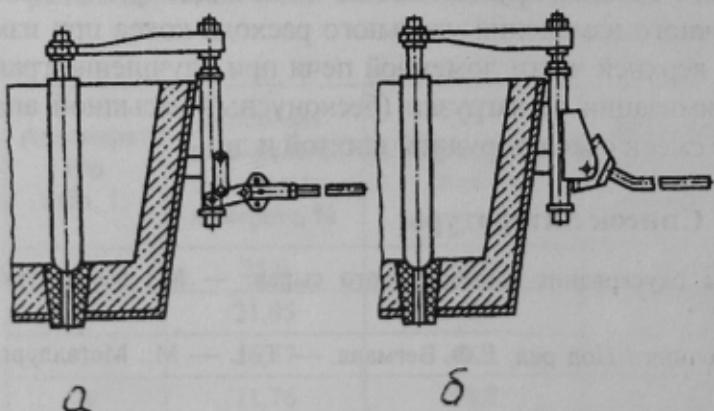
Схемы стопорных механизмов промежуточных ковшей МНЛЗ: а — с рычажной системой; б — с реечной передачей
